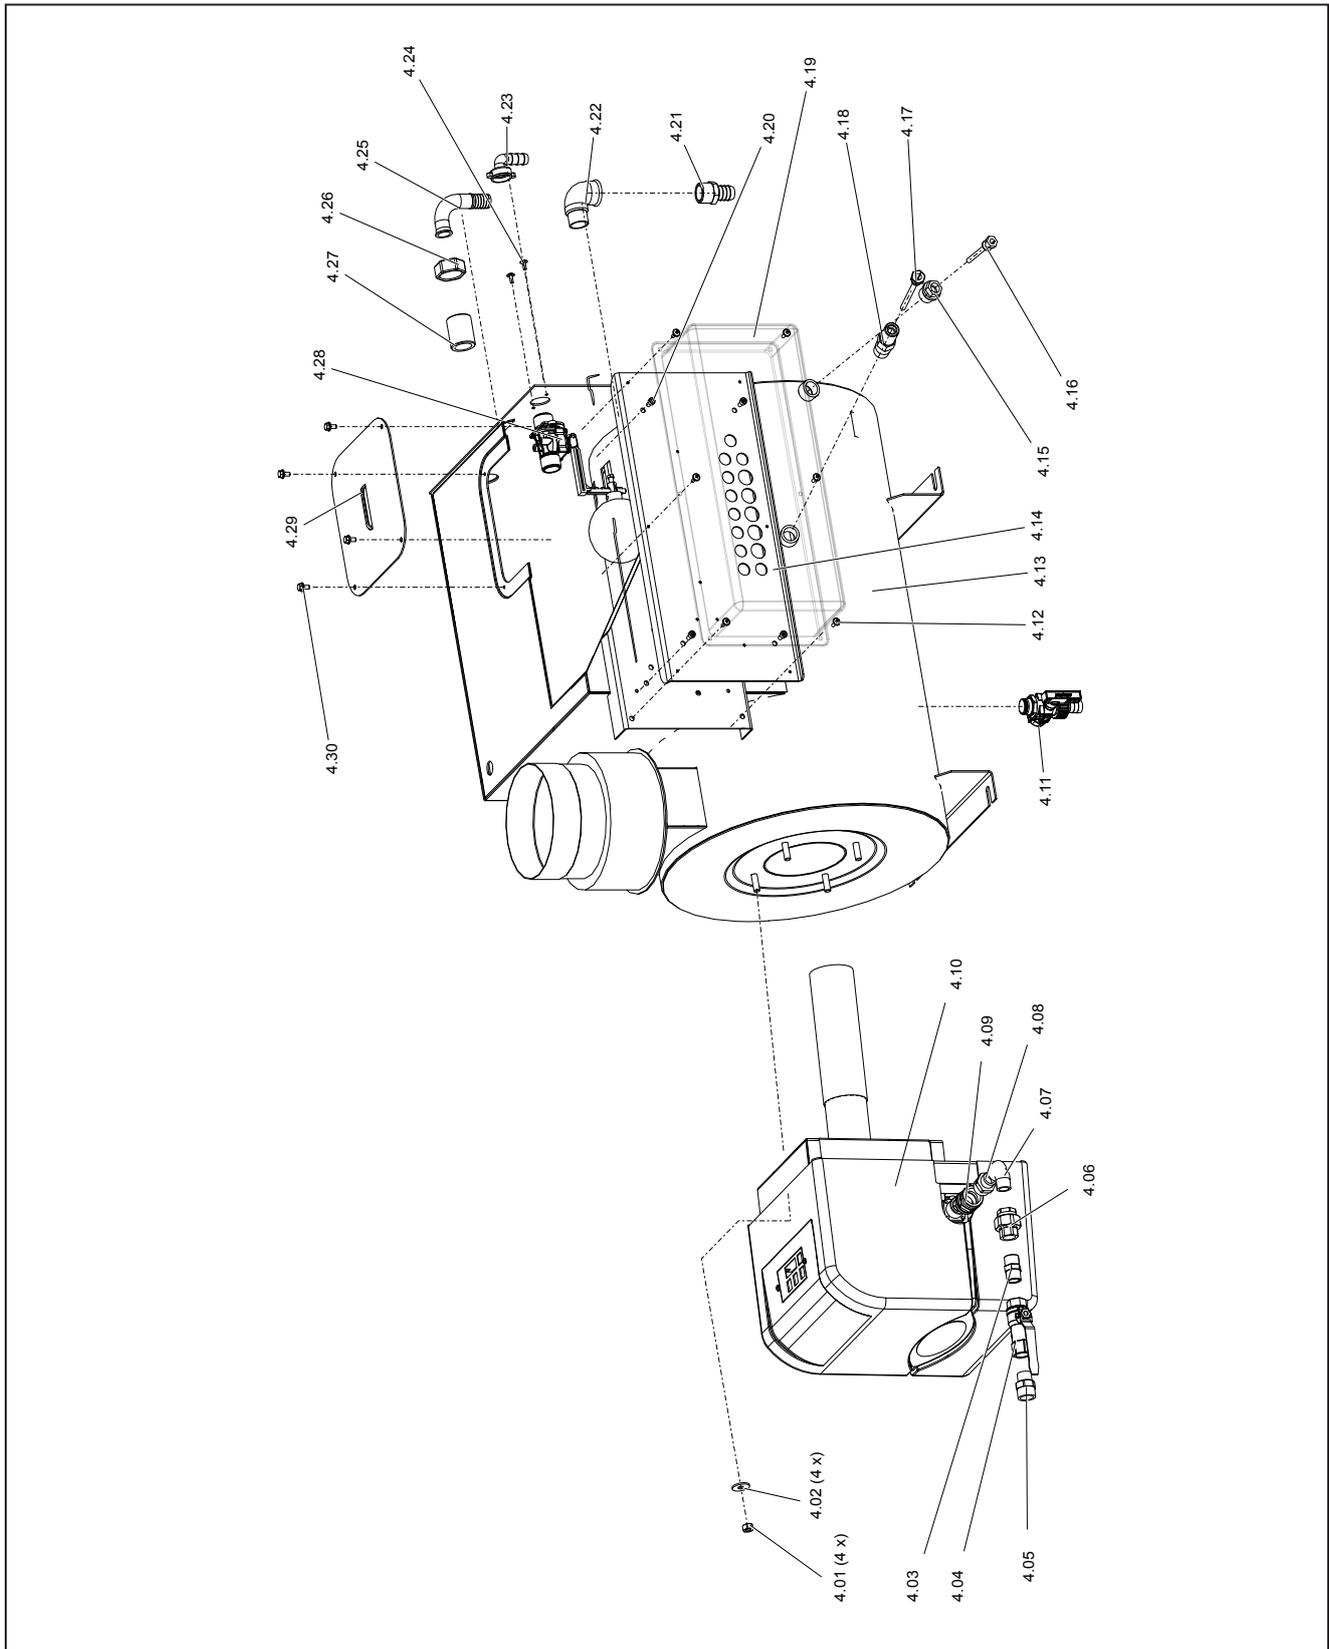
5 Baltur Gasbrenner mit Boilersystem, Explosionszeichnung
